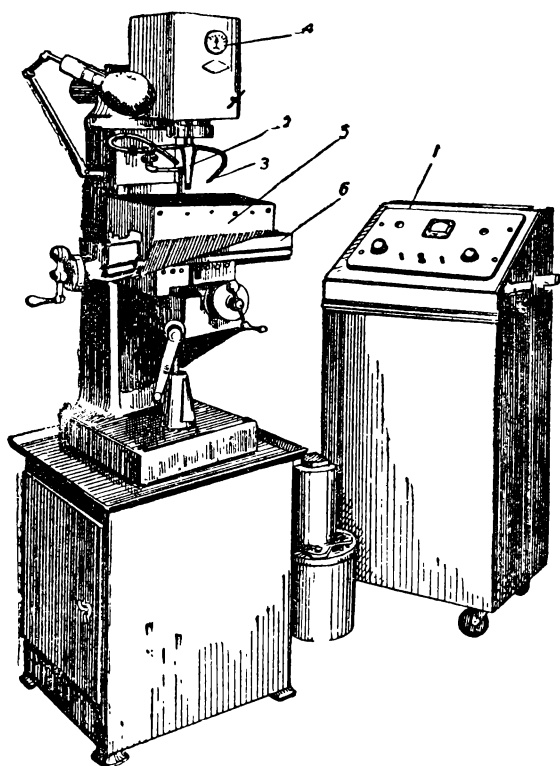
Внешний вид машины для ультразвуковой обработки хрупких материалов:
